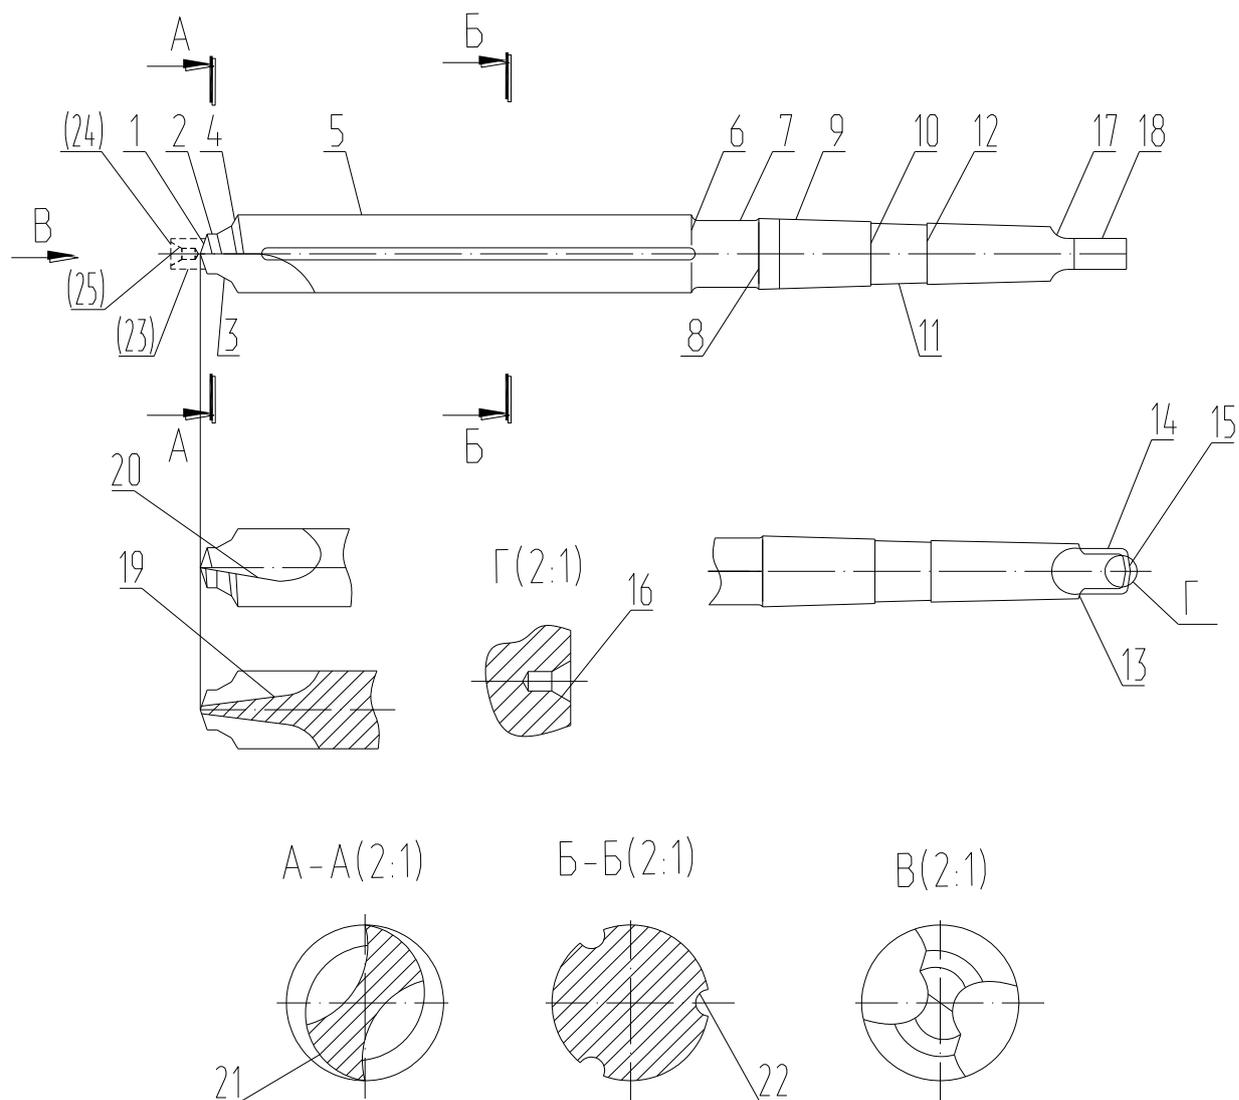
Систематизация поверхностей детали «Сверло центровочное».
